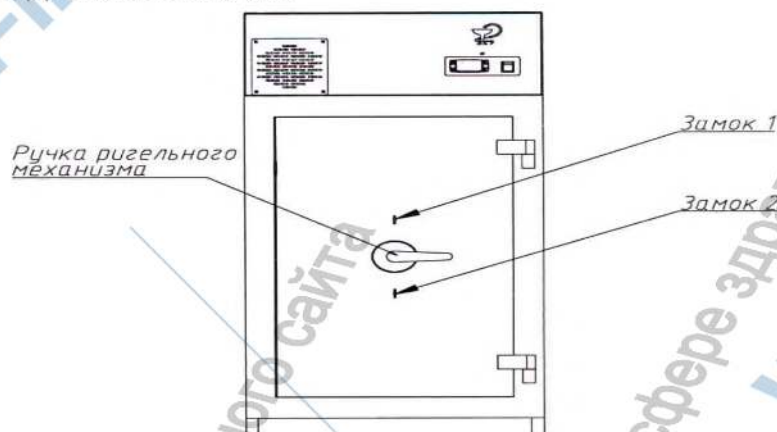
Общий вид расположения замков и ручки ригельного механизма для СХ с двумя замками.
